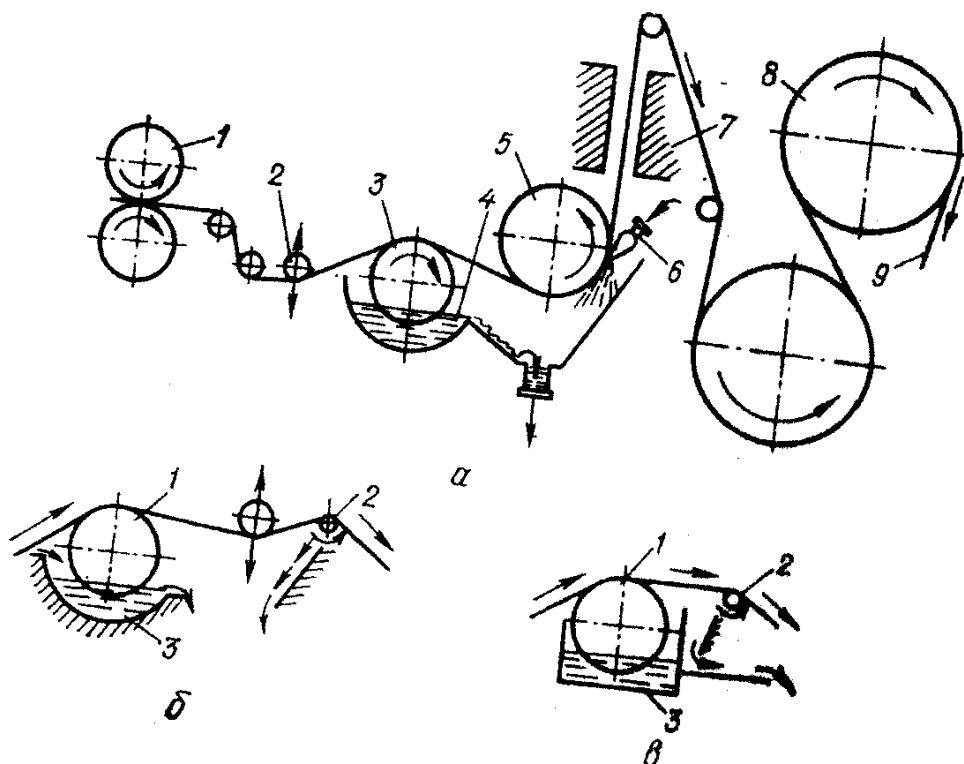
Схемы меловальных устройств: *а* – с воздушным шабером: 1 – полусухой каландр; 2 – разгонный валик типа Маунт-Хоуп; 3 – наносящий валик; 4 – ванна; 5 – прижимной валик; 6 – сопло воздушного шабера; 7 – сушилка с инфракрасным излучением; 8 – сушильный цилиндр; 9 – полотно бумаги; *б* – с вращающимся стержнем: 1 – наносящий валик; 2 – вращающийся стержень (пруток); 3 – ванна; *в* – с роликовым шабером: 1 – наносящий валик; 2 – роликовый шабер; 3 – ванна
